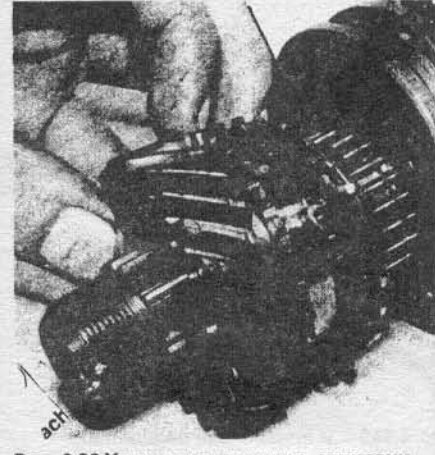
Установка пружины синхронизатора и шестерни четвертой передачи.
